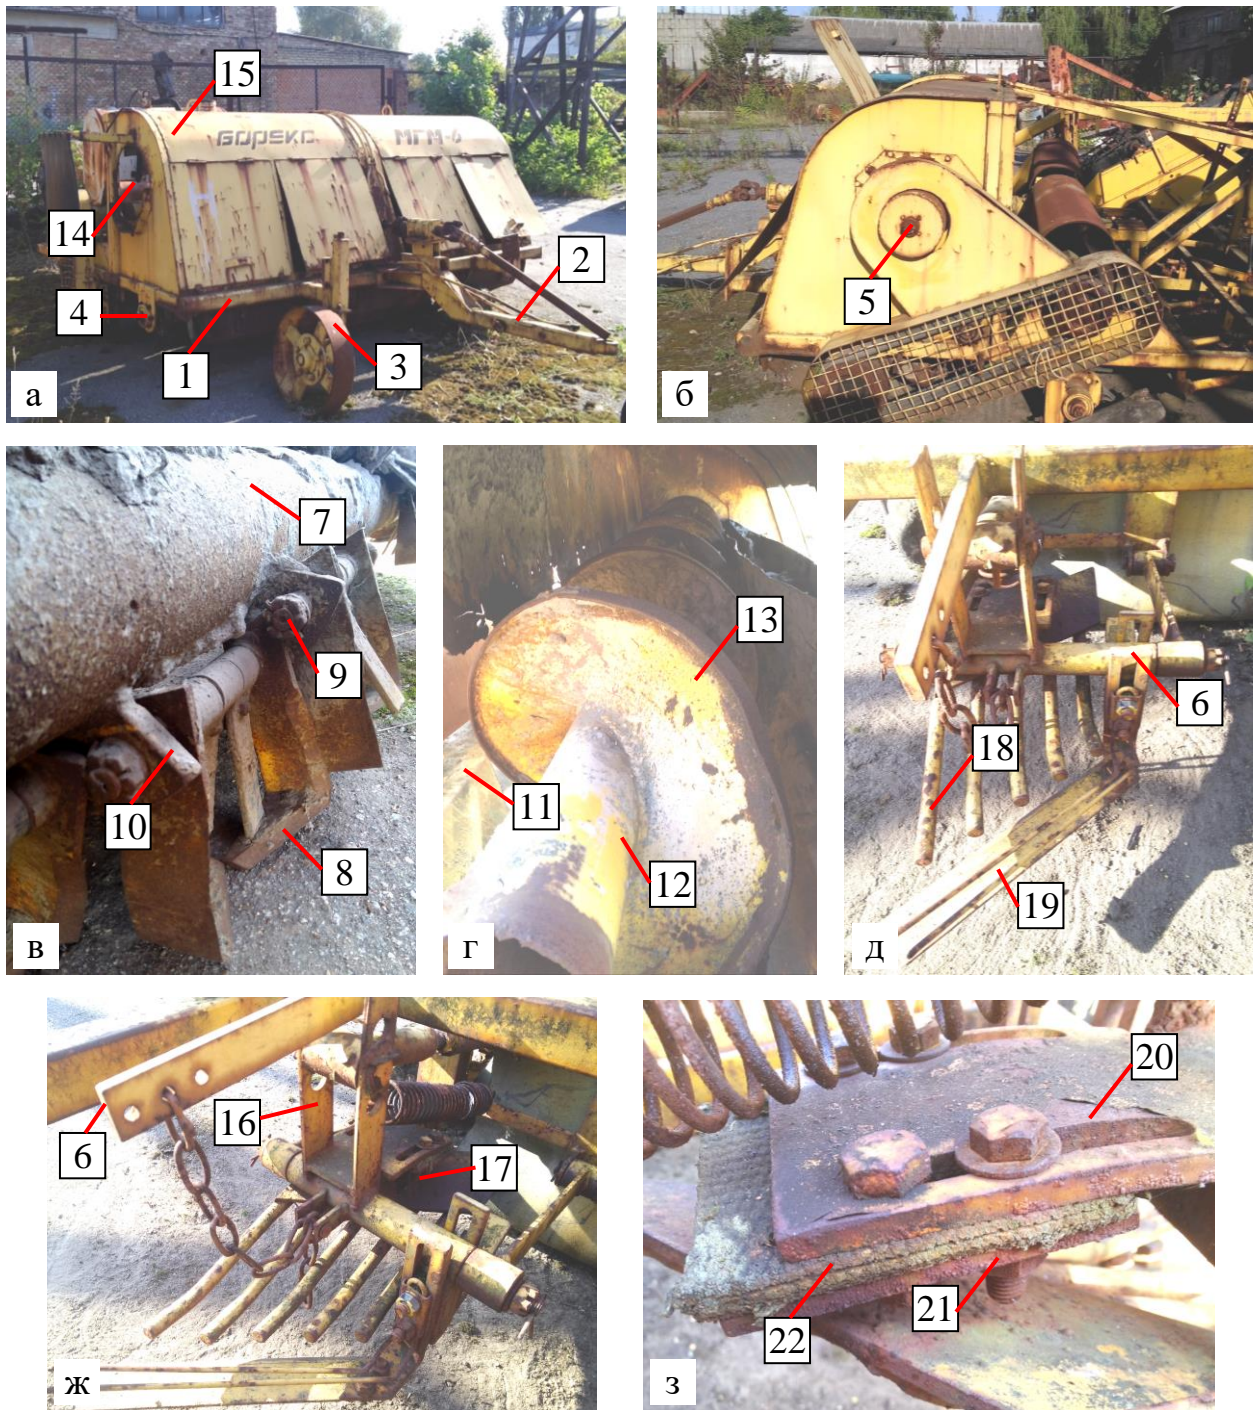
Загальний вигляд гичкозбирального модуля (а, б – вигляд спереду та збоку) та робочих органів: в – роторного гичкоріза, вигляд збоку; г – гвинтового конвеєра; д, ж – обрізника залишків гички, вигляд спереду; 1 – рама; 2 – сниця; 3 – колесо; 4 – роторний гичкоріз; 5 – гвинтовий конвеєр; 6 – обрізник; 7, 12 – барабан; 8 – ніж; 9 – палець; 10 – опорна пластина; 11 – жолоб; 13 – виток; 14 – вихідна частина гвинтового конвеєра; 15 – кожух; 16 – паралелограмна підвіска; 17 – кронштейн; 18 – копір; 19 – ніж; 20, 21 – пластина кронштейна; 22 – пружна прокладка
